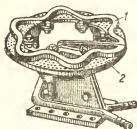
Индуктор для закали торцевой поверхности способом одновременного нагрева при вращении детали:
